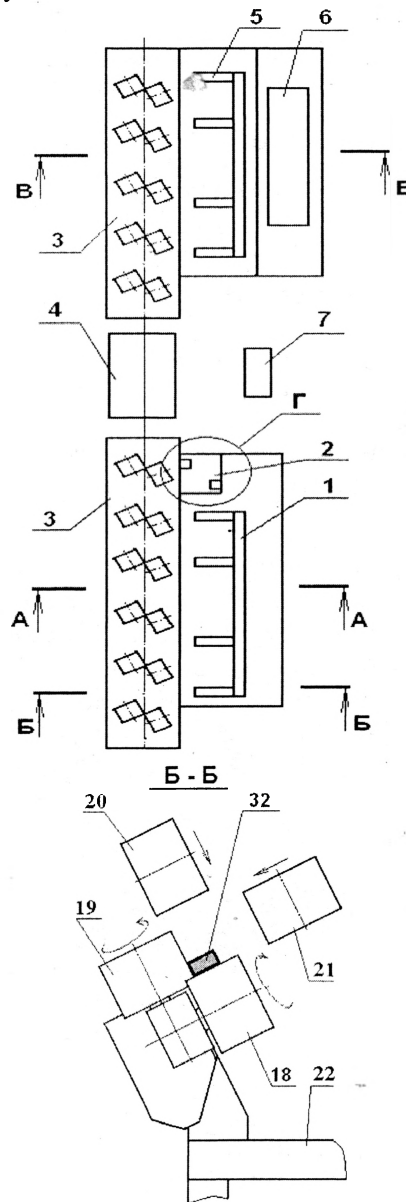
Схема установки для термической обработки стального прямоугольного проката: 1 — механизм загрузки; 2 — механизм контроля торцевого зазора; 3 — подающий конвейер; 4 — индуктор; 5 — механизма выгрузки; 6 — механизм складирования; 7 — пульт управления; 18 и 19 — приводные ролики; 20 и 21 — прижимные ролики; 22 — рама
